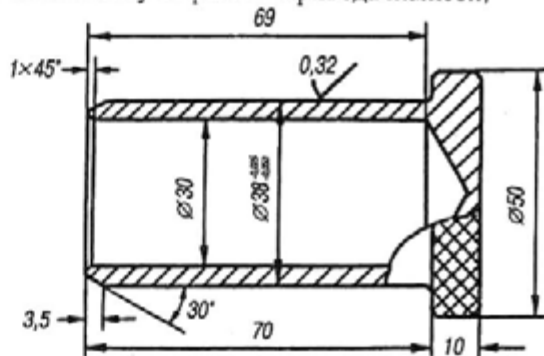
Пробка-заглушка в удлинителе коробки передач
